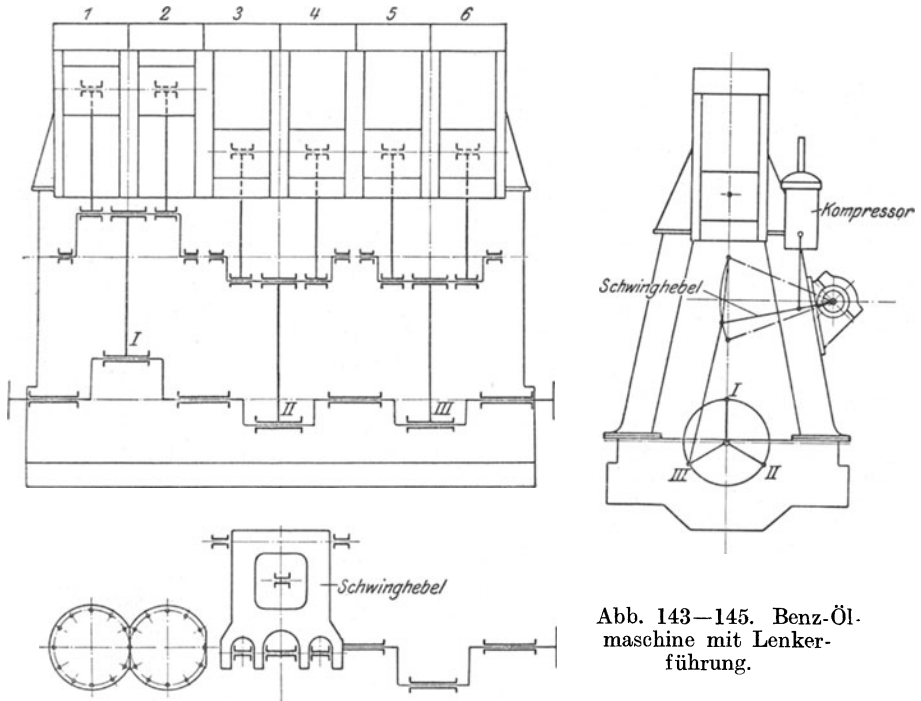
145. Benz.-Ölmaschine mit Lenkerführung.
